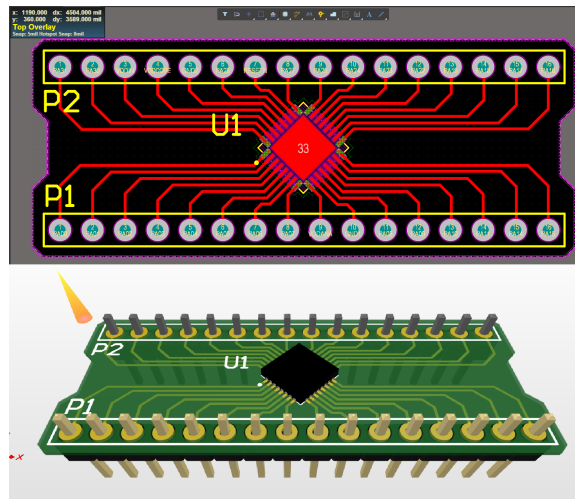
Diseño PCB prototipo para SAMD21E18A encapsulado QFN.
